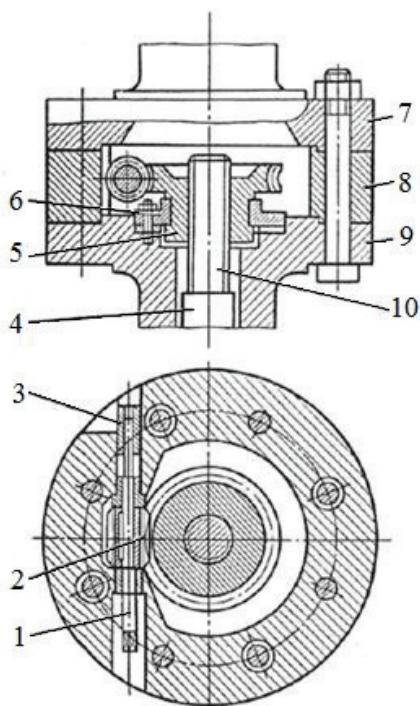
Схема ручного привода механизма разворота лопастей:
